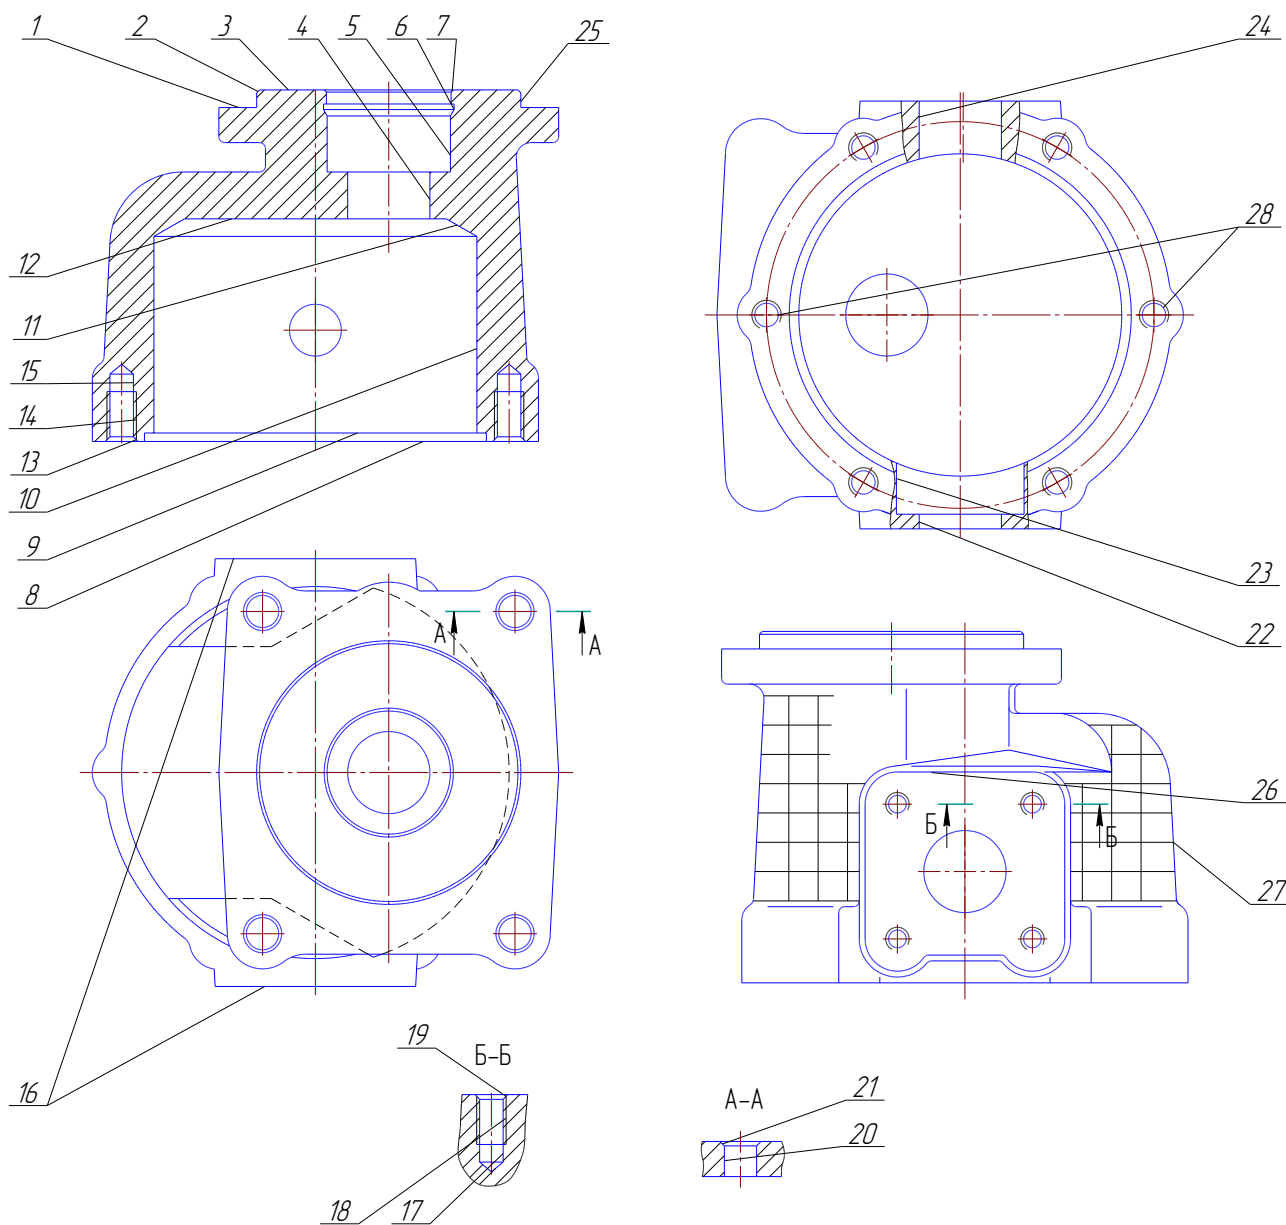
Спрощений ескіз деталі корпус НШ32-3-01
